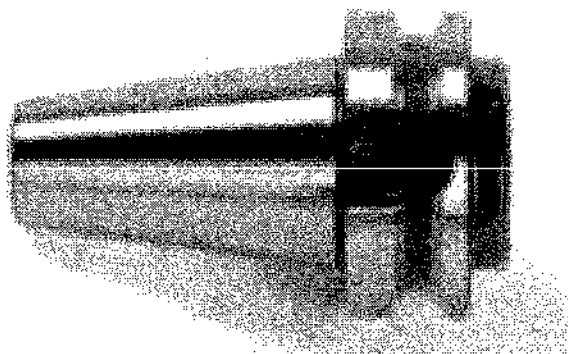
Оправка для концевой фрезы Weldon H35 D20
